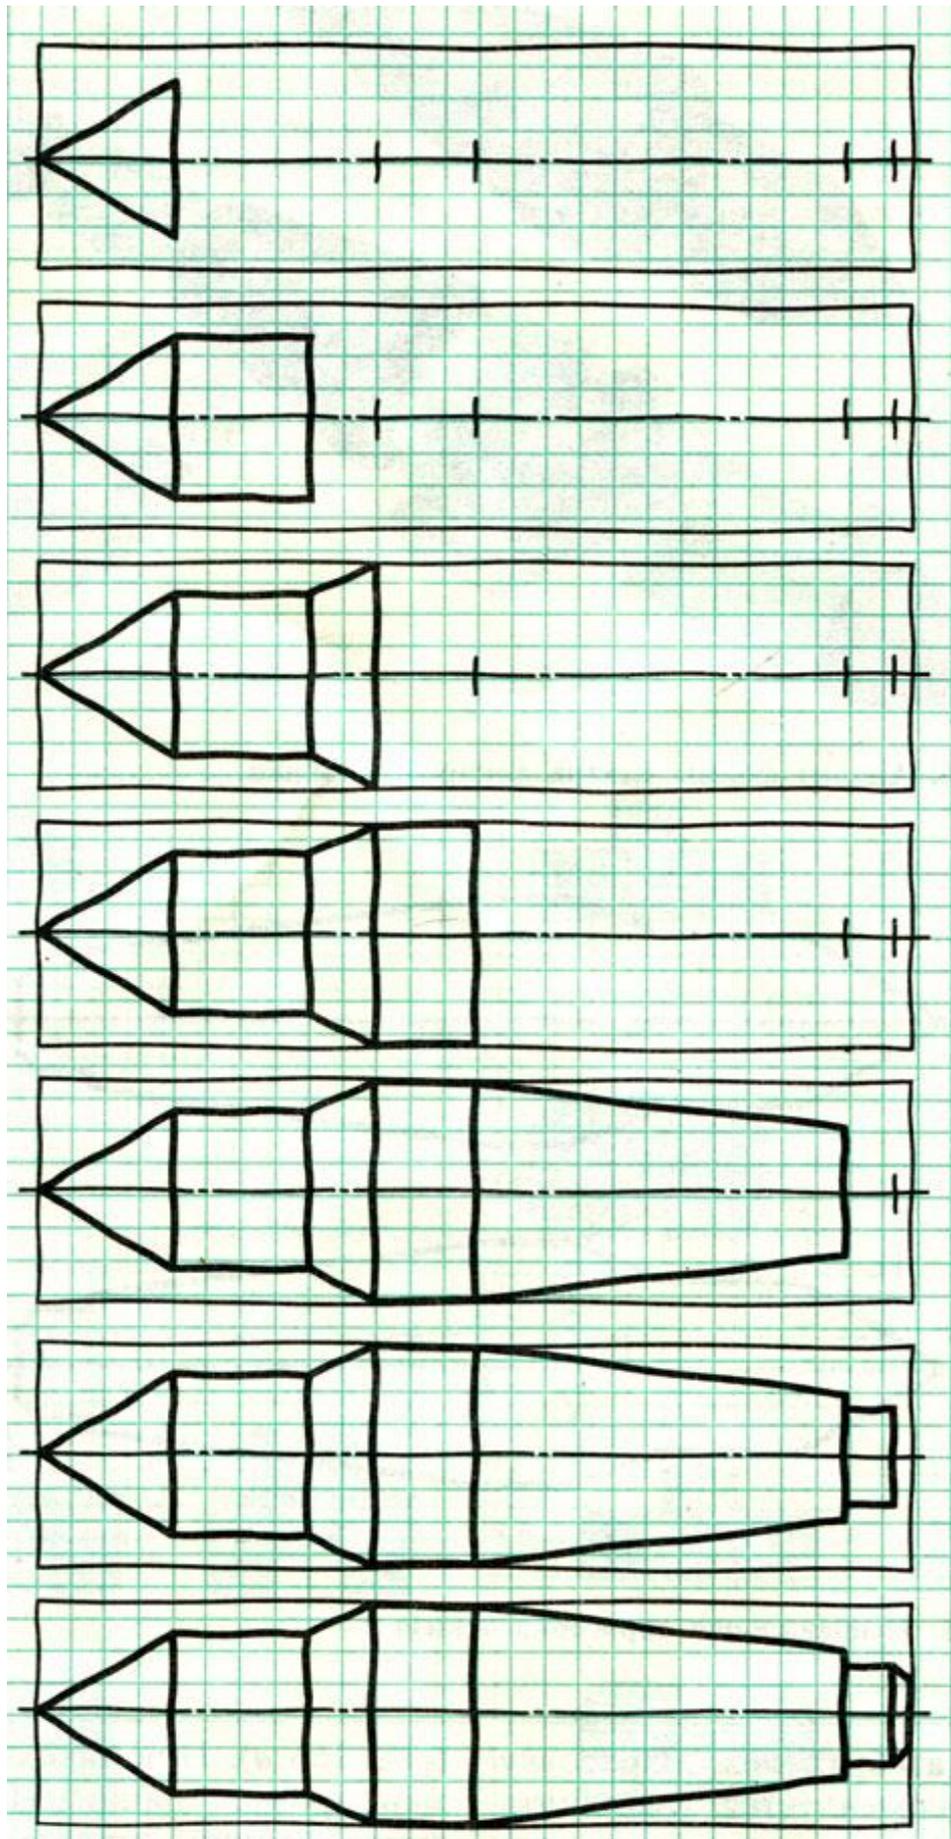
Последовательность зарисовки эскиза центра токарного станка
